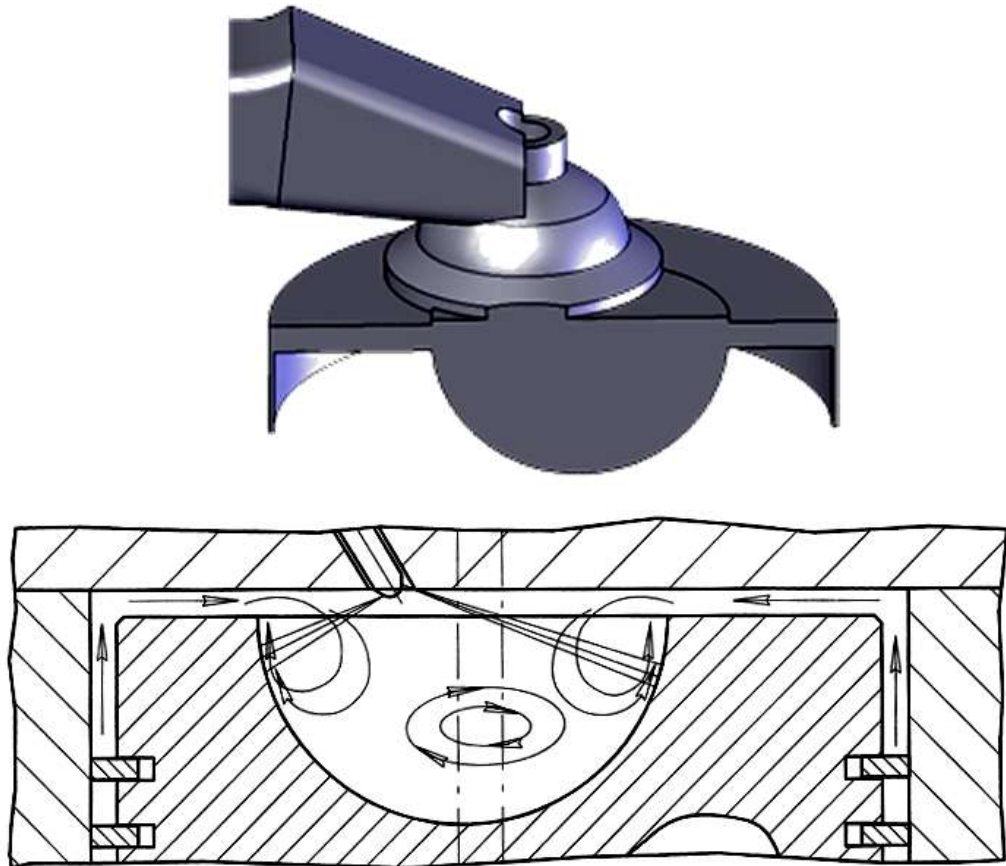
Ділянка розрахункової області, що описує кільцевий зазор між бічною поверхнею головки поршня й дзеркалом циліндра
